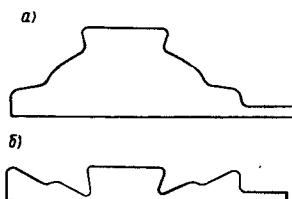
Мех-насос со ступенчатым формованным корпусом: *a* – нерабочее положение; *b* – рабочее положение
